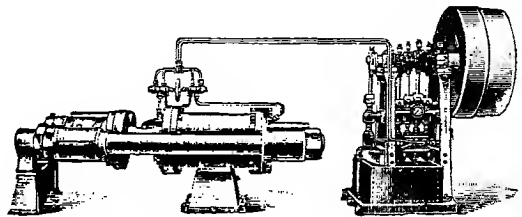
Horizontale Strangpresse für Licht- und Batteriekohlen mit hydraulischer Pumpe.
